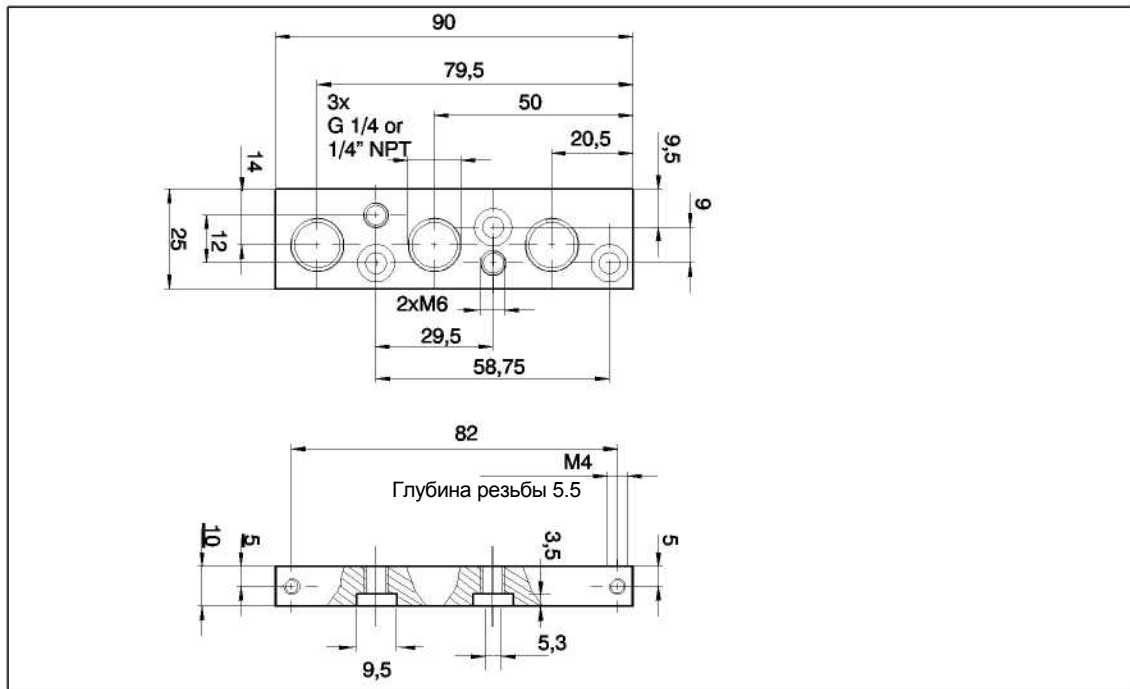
Размерный чертёж клеммника для пластикового корпуса
